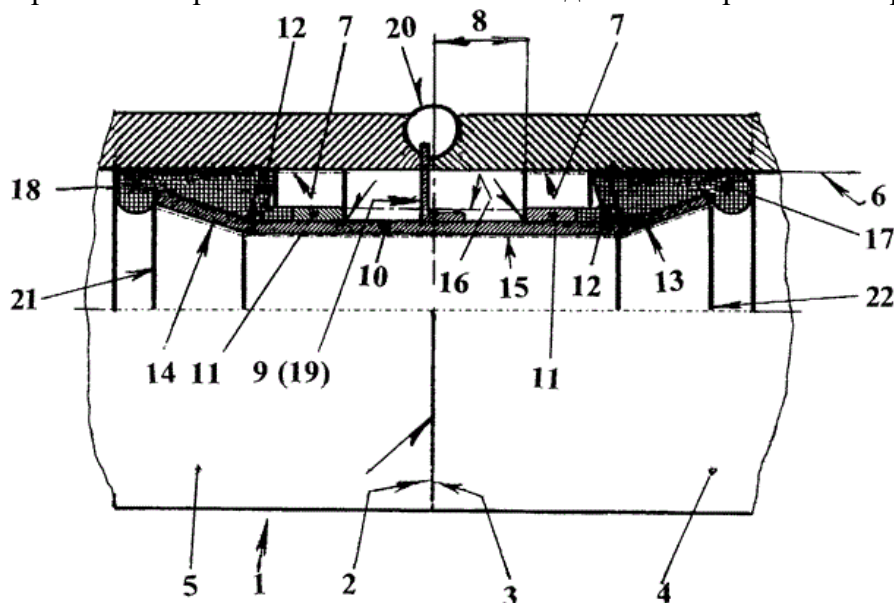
Чертеж продольного сечения сварного соединения трубопроводов с использованием изоляционной втулки и антикоррозионного покрытия
